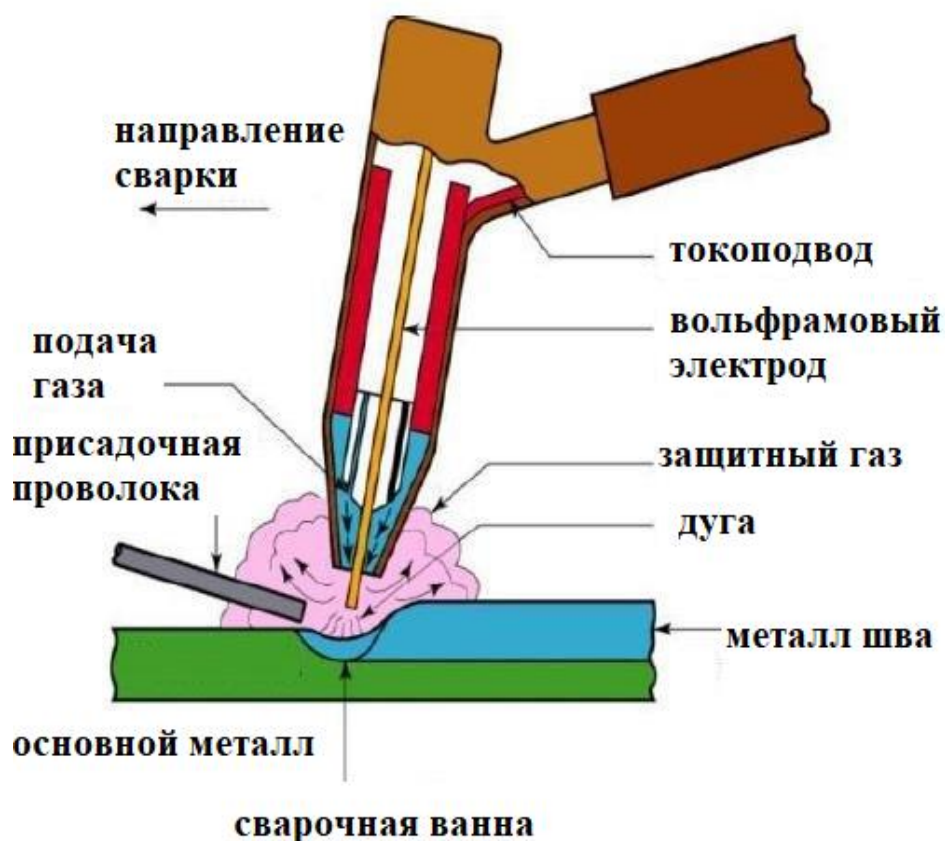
Схема выполнения аргодуговой сварки неплавящимся электродом
